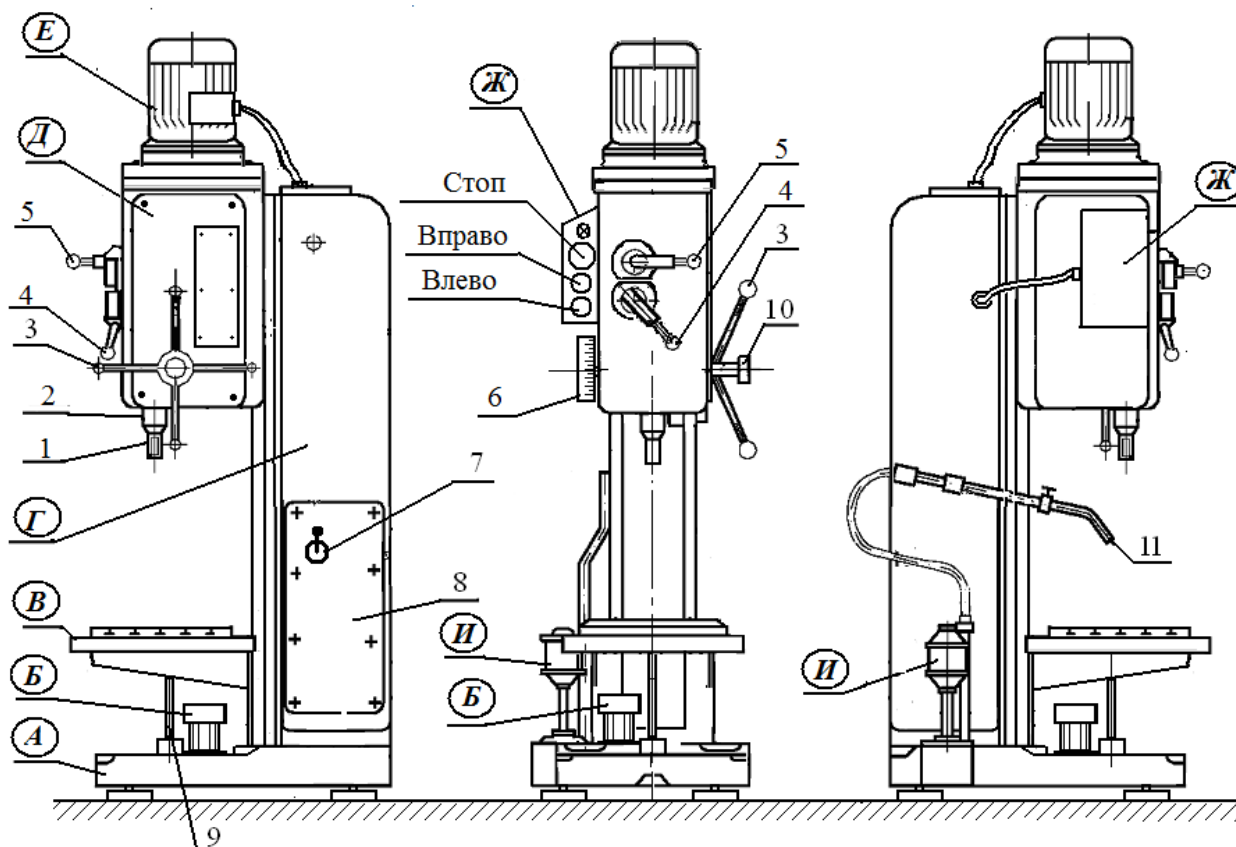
Общий вид вертикально-сверлильного станка 2Н18
